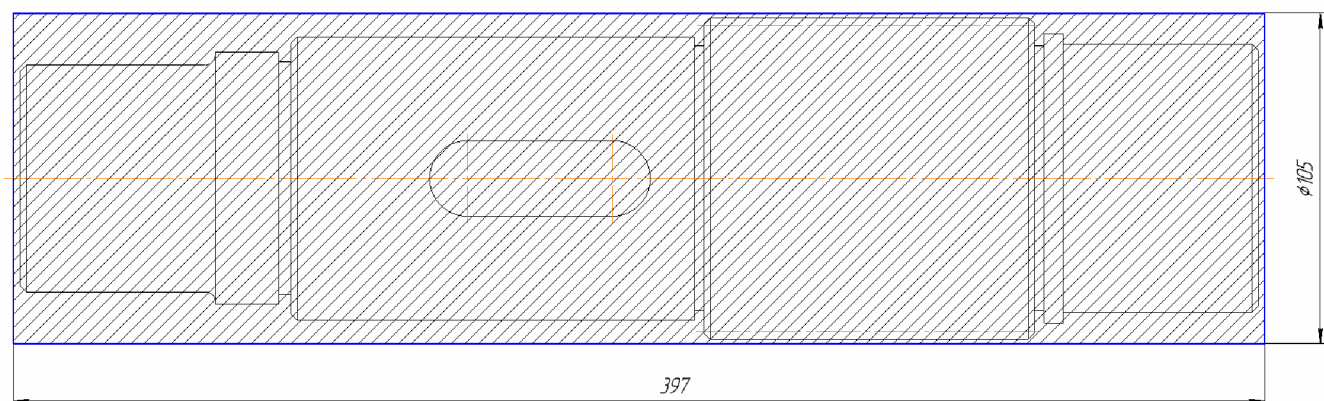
Ескіз заготовки, що виготовлена з прокату
